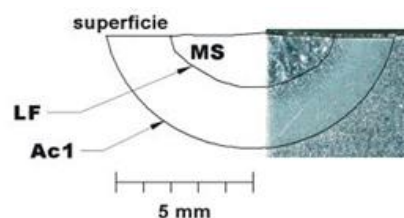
Macrografía de la sección transversal de la soldadura TIG autógena en acero AISI P20 con energía de 10 kJ/cm
